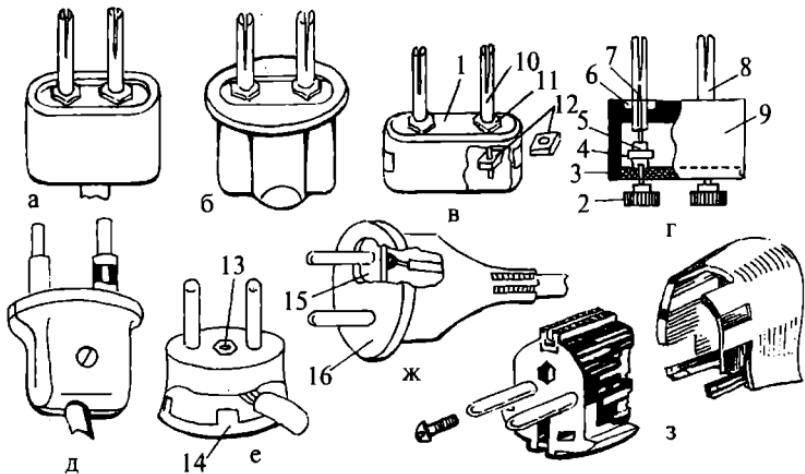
Типы и устройство штепсельных вилок: а, б — с разрезными штифтами и пластмассовым корпусом; в — с разрезными штифтами и керамическим корпусом; г — с разрезными штифтами и разборным пластмассовым корпусом; д — с цельными штифтами и разборными пластмассовыми половинками корпуса; е — с цельными штифтами и крышкой пластмассового корпуса; ж — с цельными штифтами и неразборным резиновым или пластмассовым корпусом; з — двухполюсная с боковыми заземляющими контактами; 1 — планка; 2 — пластмассовый барашек; 3 — остав; 4 — гайка круглая нормальная; 5 — втулка; 6 — гайка круглая; 7 — стальная игла; 8 — разрезной полый штифт; 9 — верх корпуса; 10 — разрезной штифт; 11 — гайка шестигранная; 12 — гайка закладная; 13 — винт центральный; 14 — крышка корпуса; 15 — планка пластмассовая; 16 — резиновый или пластмассовый корпус
